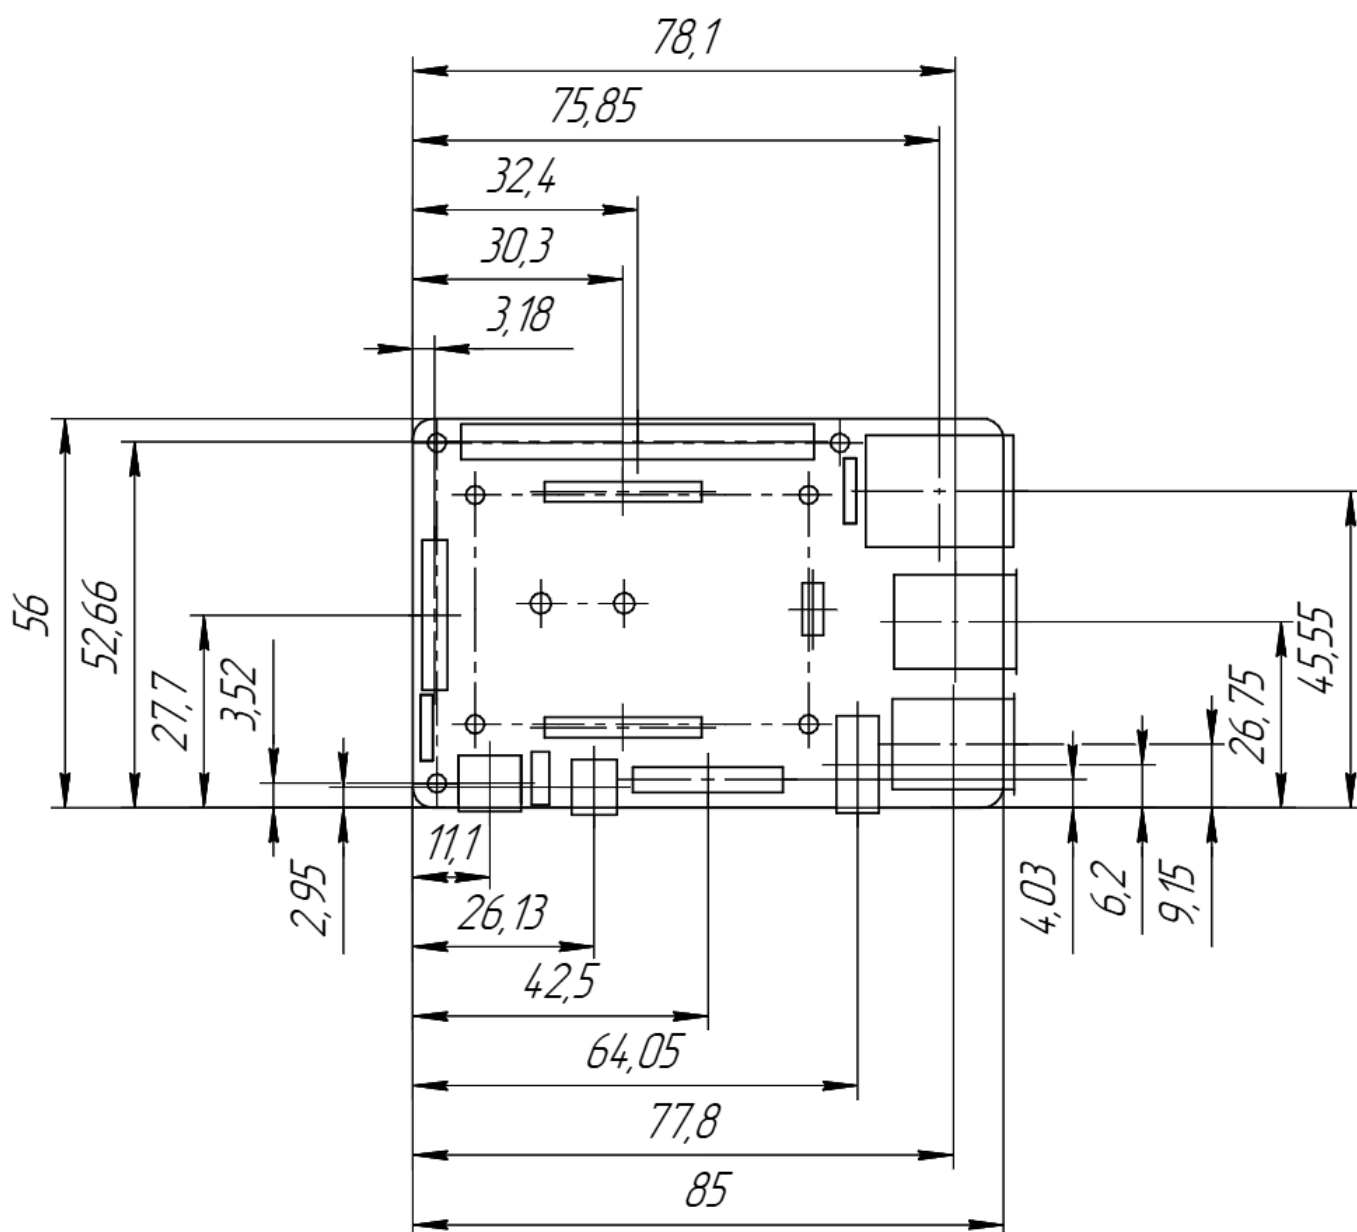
Чертеж ELTAY RM66, вид сверху.
